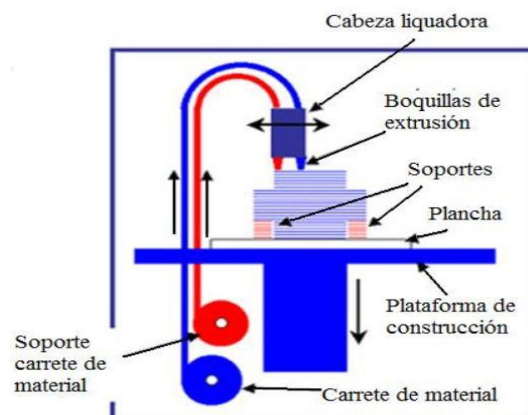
Proceso de fabricación mediante modelado por deposición fundida (FDM) [11]
